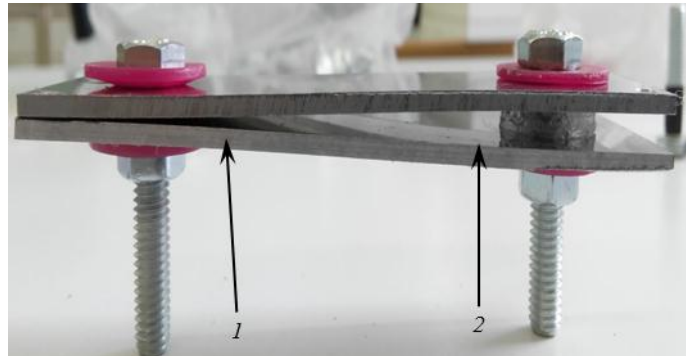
Внешний вид собранного пакета, используемого для проведения натуральных испытаний на щелевую коррозию по ГОСТ 9.909–86:
